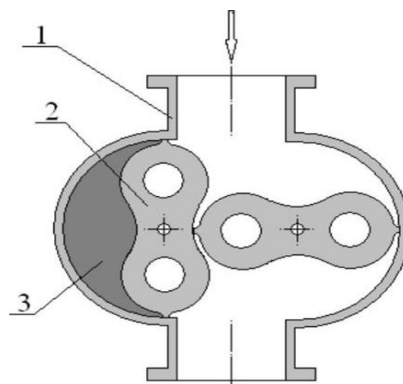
Ротаційний лічильник газу: 1 – корпус, 2 – ротор, 3 – вимірювальний обсяг
